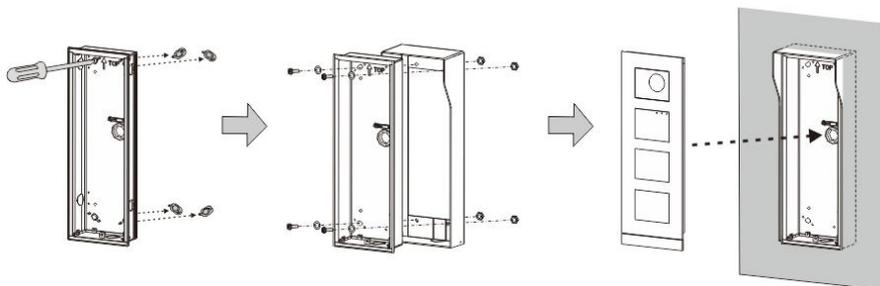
Монтаж в корпусе для установки с утапливанием с козырьком
